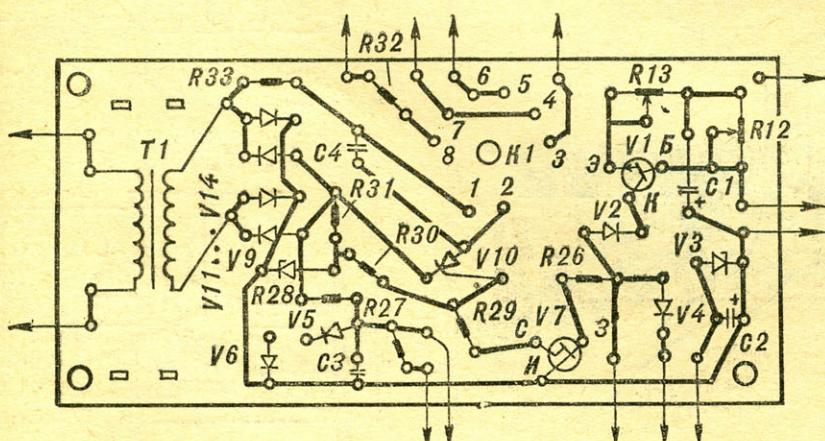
Печатная плата фотоприбора с расположением деталей.
